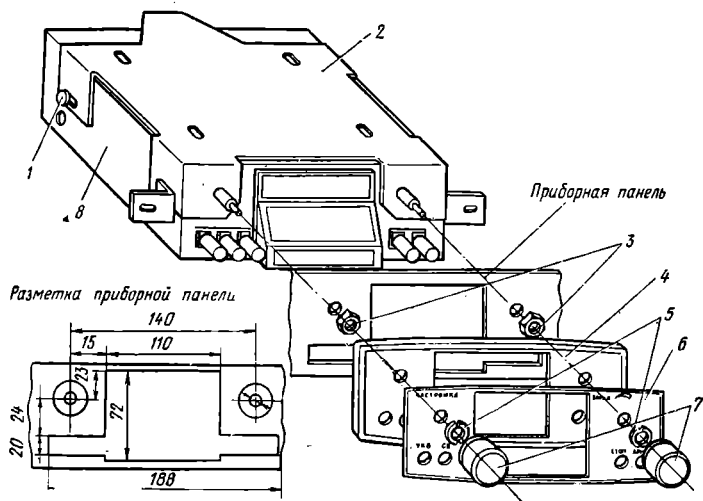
Установка и крепление магнитолы АМ-301 в автомобиле
